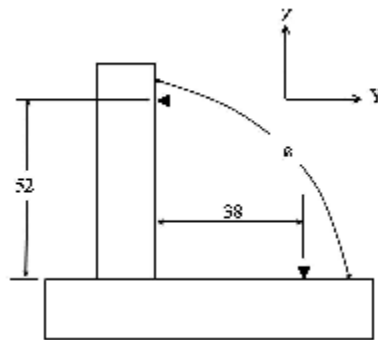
Medição do ângulo da junta após a soldagem (junta restringida).
